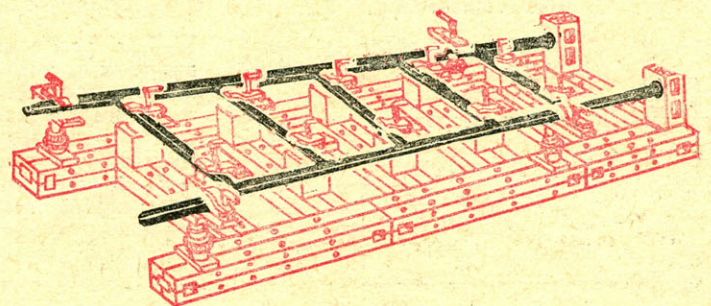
Универсально-сборное приспособление для сварки лестницы.
